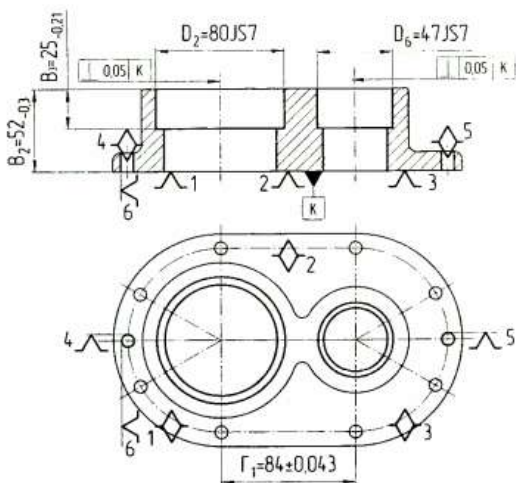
Схема базування під час отримання поверхонь деталі на останніх етапах оброблення
